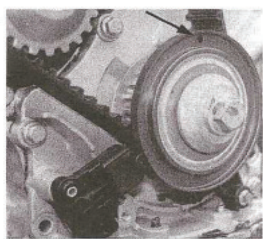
Стрелка указывает на отверстие-метку для монтажа зубчатого ремня
